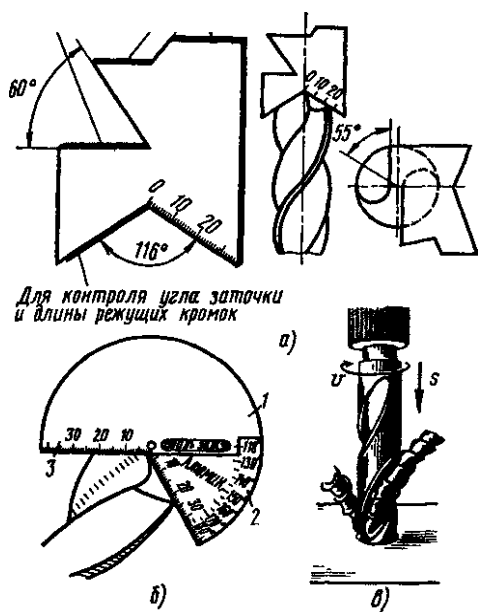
Проверка качества заточки сверла: *а* — по шаблону, *б* — универсальным угломером, *в* — пробным сверлением
